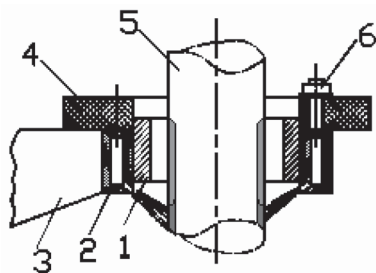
Индукционный виток индуктора для закалки трубы гидроцилиндра подъема платформы самосвала МАЗ-5551 с закрепленным на нем кольцом жесткости: 1 – индукционный виток; 2 – трубка охлаждения; 3 – шина; 4 – кольцо жесткости; 5 – закаливаемая деталь; 6 – детали крепежа кольца жесткости
